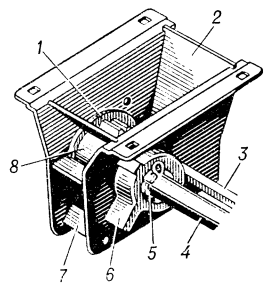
Катушечный высевающий аппарат: 1 — катушка; 2 — корпус (коробка); 3 — валик клапанов для опораживания коробки от семян; 4 — приводной валик катушки высевающих аппаратов; 5 — регулировочная шайба; 6 — муфта; 7 — доннышко; 8 — розетка.
